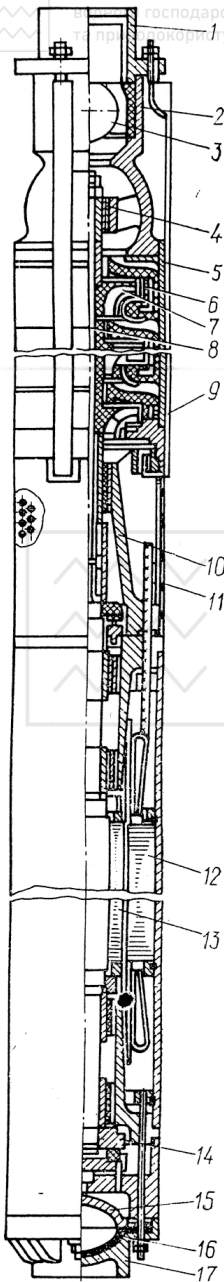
Насос з занурювальним приводом (тип ЭЦВ): 1-напірний патрубок; 2- корпус радіального підшипника; 3- кульовий зворотний клапан; 4- підшипник; 5- корпус ступеня; 6- напрямний апарат; 7- робоче колесо; 8- радіальний підшипник; 9- стяжка; 10- підвід; 11- решітка; 12- статор електродвигуна; 13- ротор електродвигуна; 14- радіально-упорний підшипник ковзання; 15- діафрагма; 16- шпилька; 17- днище
